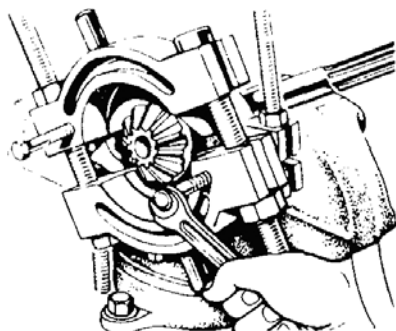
Спрессовка подшипников № 7507 с полуоси или вертикального вала.
